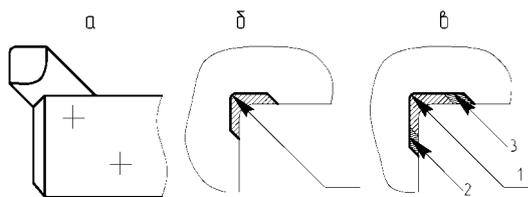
Типовые схемы обработки наружных угловых канавок для выхода шлифовального круга: а) Резец; б) Однопроходная обработка; в) Трехпроходная обработка
